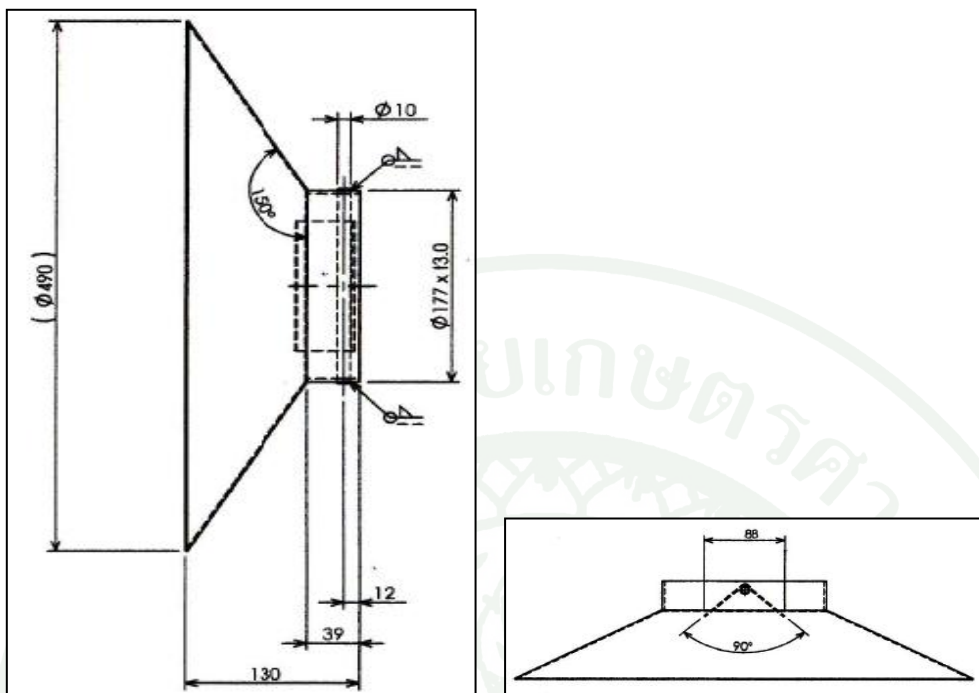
Exhaust hood ลักษณะการมองแบบด้านบน (Top view)
